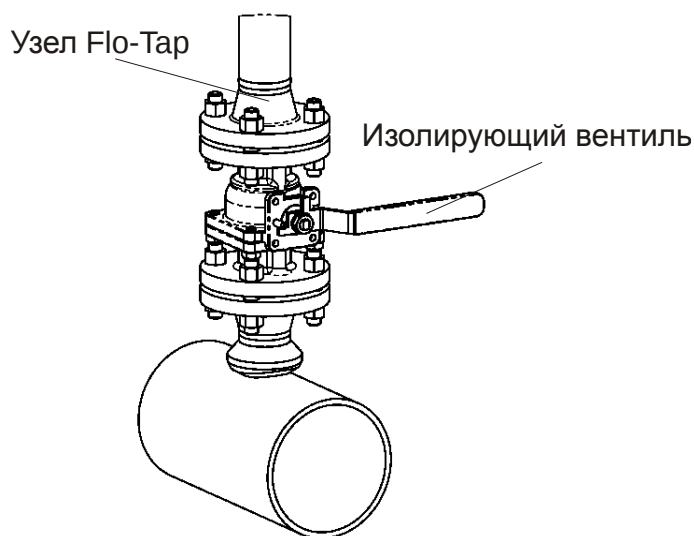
Установка полной сборки Flo-Tap на изолирующий вентиль
